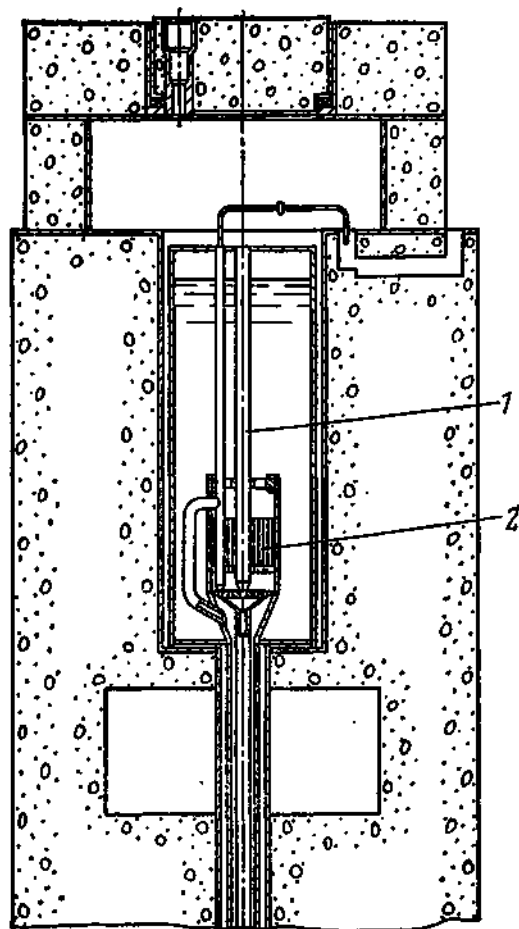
Компоновка механизма СУЗ на исследовательском реакторе ВВР-Ц:
